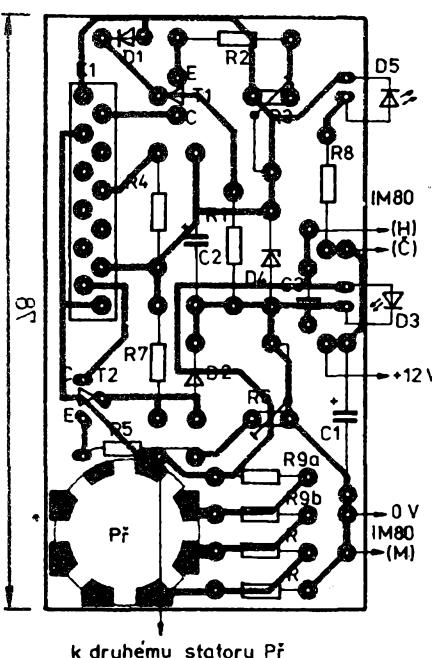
Obrazec plošných spojů kontaktní destičky (X23)
